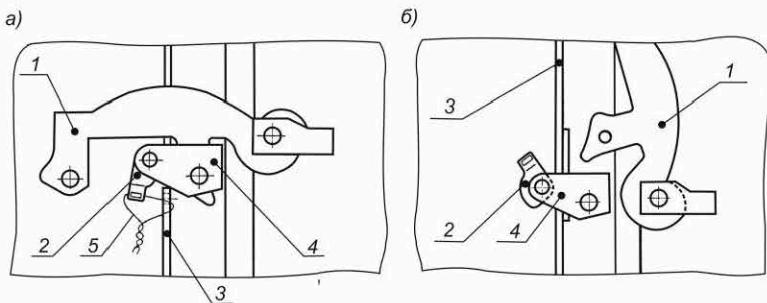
Запорное устройство дверей в закрытом (а) и открытом (б) положениях закидки
